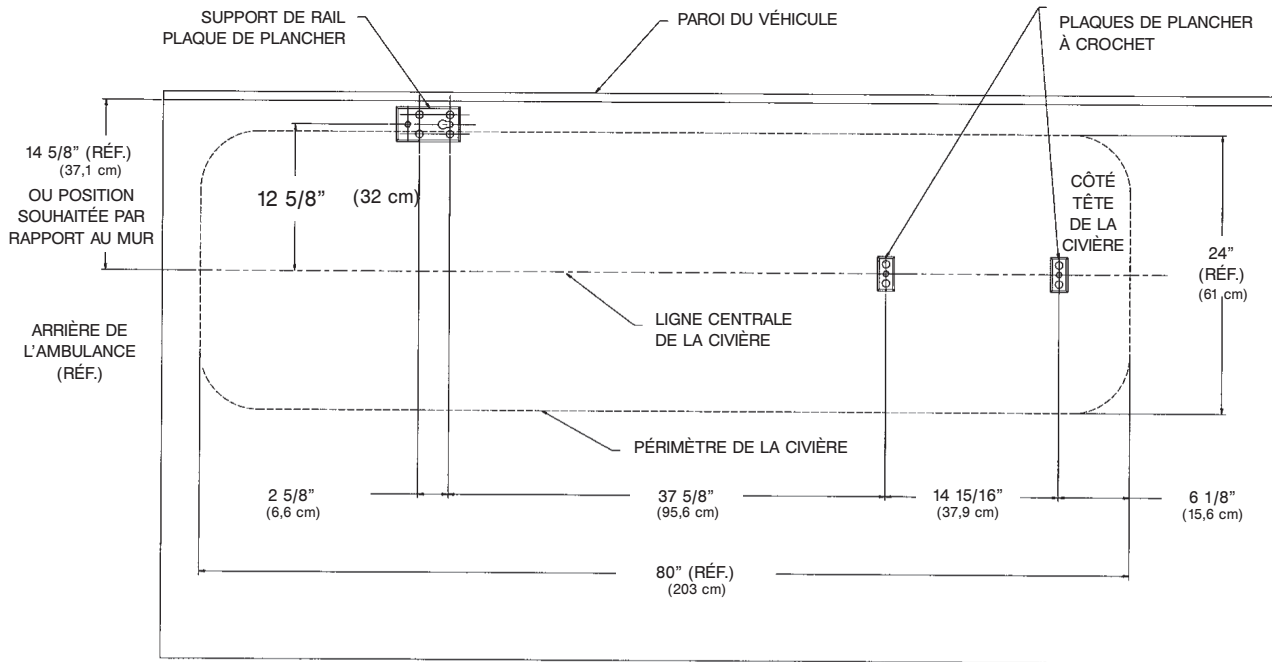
Spécifications d'installation – dispositif de fixation pour montage au sol
